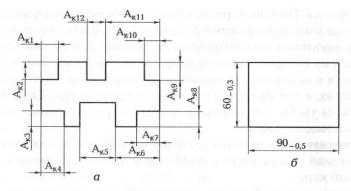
Чертеж обрабатываемой детали (а) и заготовки (б)
